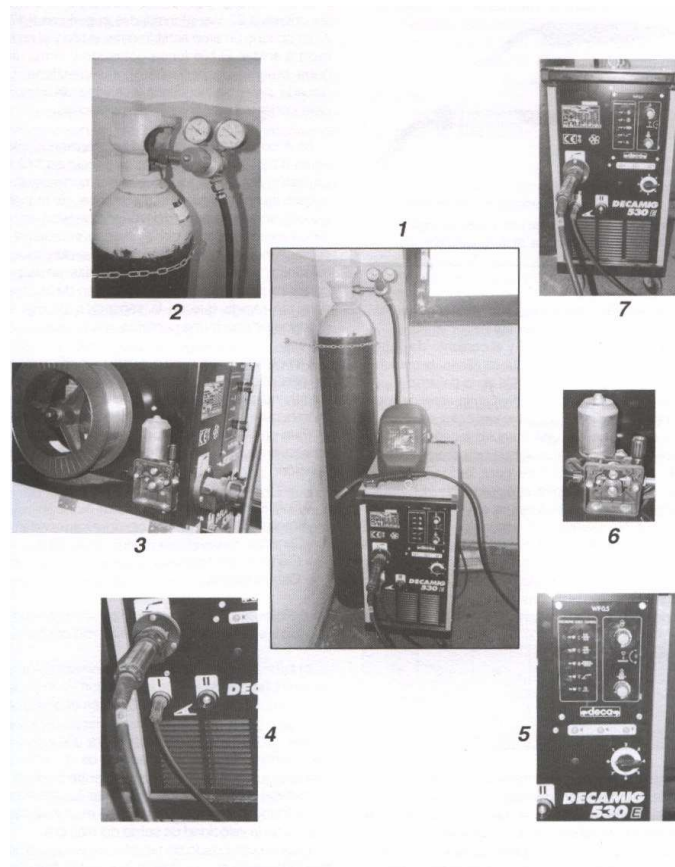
Equipo completo de soldadora MIG.
